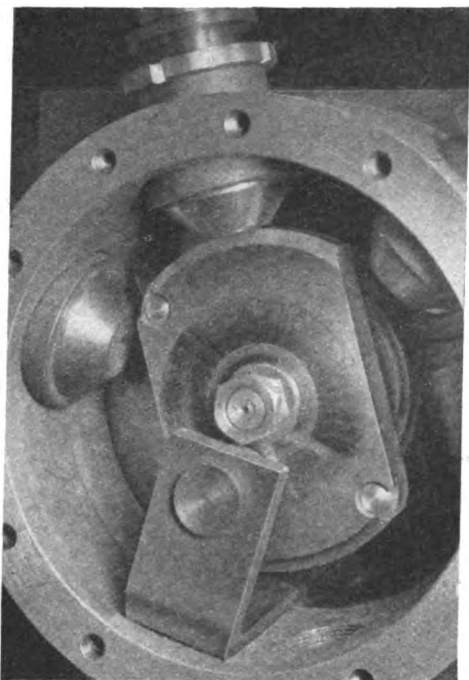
Dreiphasiger mechanischer Gleichrichter (erste Ausführungsform des Kontaktumformers); Druckgefäß geöffnet.
